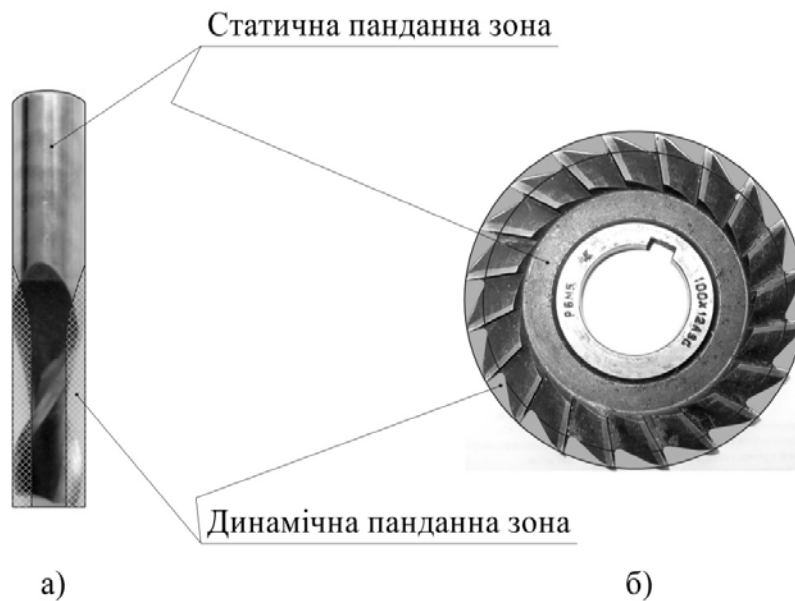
Первинні панданні зони фрезерного інструмента, де:
